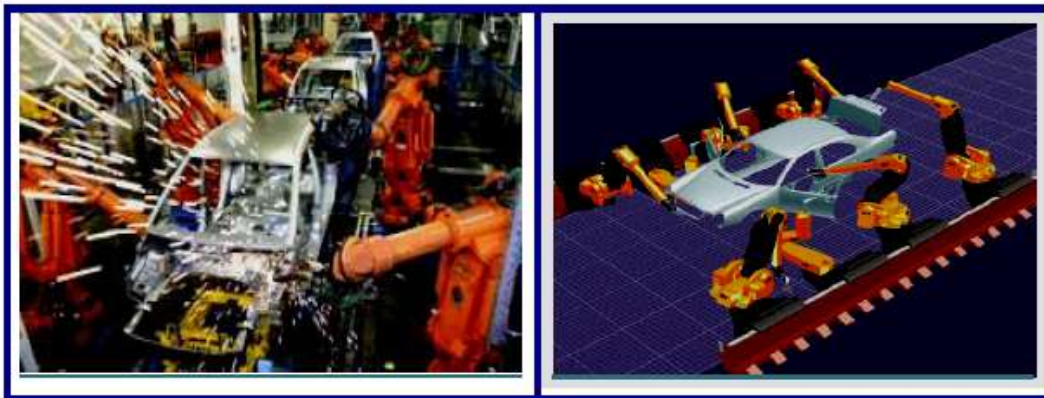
Robots industriels de soudage et de peinture
